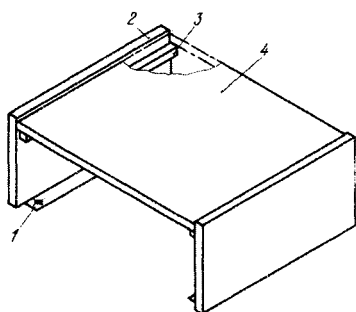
Крышка из фанеры: 1 — пластина, 2 шт., закрепить на дет. 2 шурупами; 2 — стенка боковая, 2 шт.; 3 — брусок, 2 шт.; 4 — стенка верхняя.
